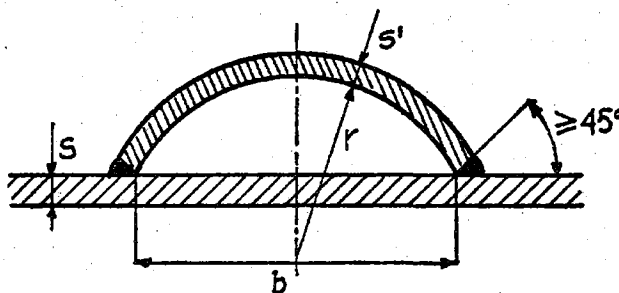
Q.1.3. - Canale a sezione di segmento circolare
